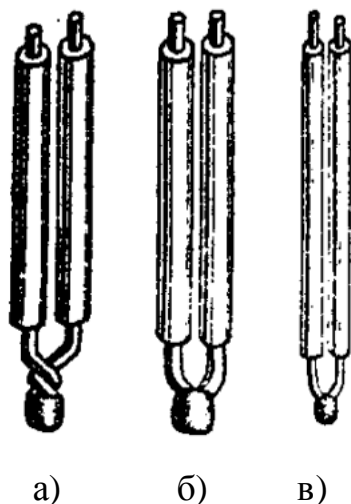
Способы изготовления рабочего конца термопары:
